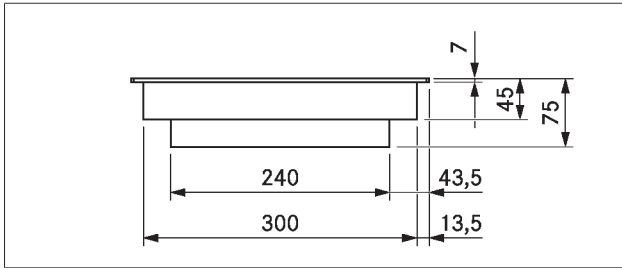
Dimensões do aparelho CKCB, vista frontal
